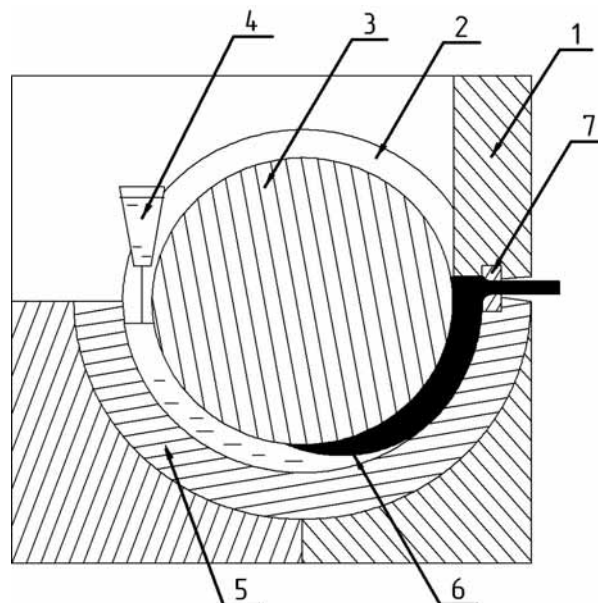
Схема установки «Conform and Castex»: 1 – разъемный корпус; 2 – канавка ротора; 3 – кольцевая вставка; 4 – литейная воронка; 5 – охлаждаемый ротор; 6 – затвердевший металл; 7 – формообразующая матрица
